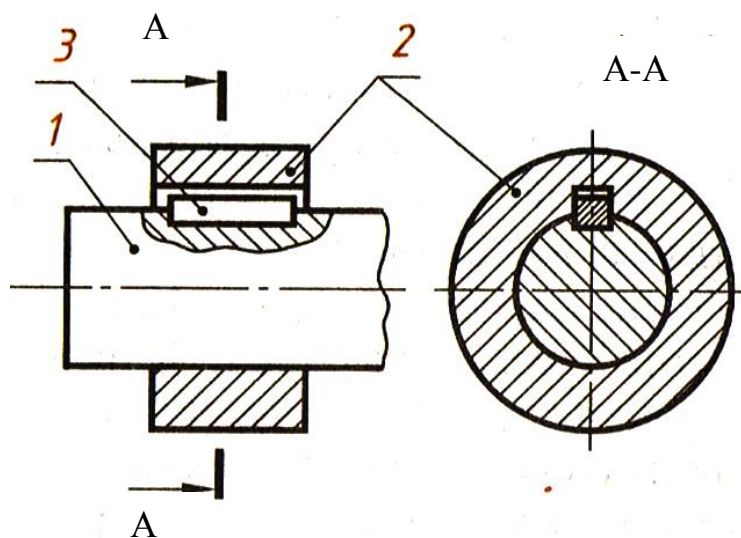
Шпоночное соединение: 1 – вал;
